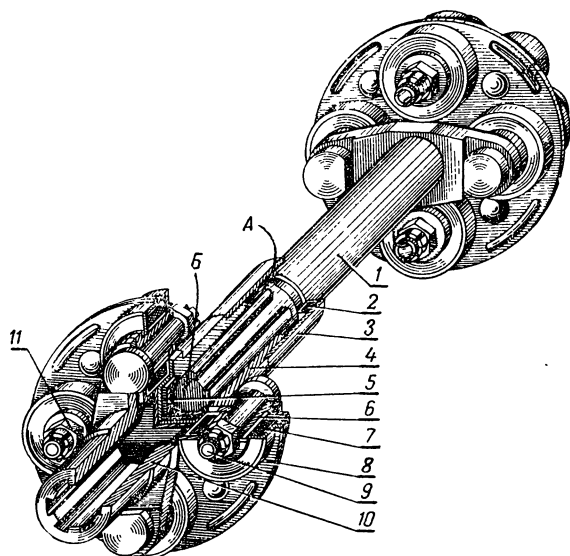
Соединительный (карданный) вал трактора ДТ-54А:
